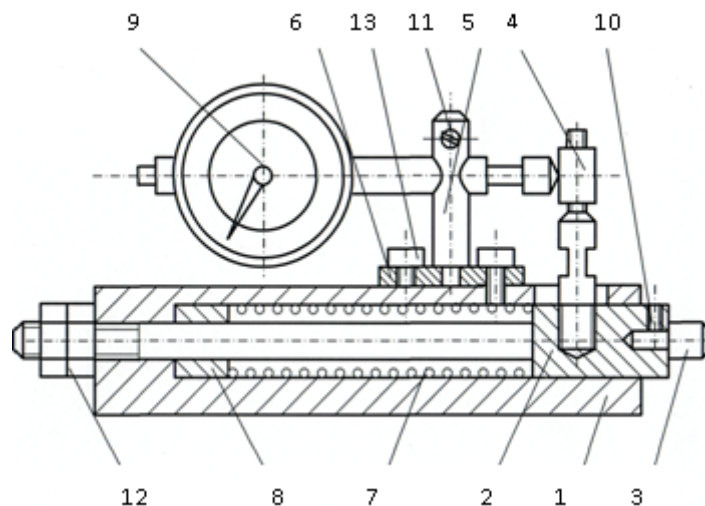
Схема алмазного выглаживателя: 1 – корпус; 2 – держатель выглаживателя; 3 – алмазный выглаживатель; 4 – стойка; 5 – стойка индикатора; 6 – основание; 7 – пружина; 8 – сменная проставка; 9 – индикатор; 10 – винт стопорный; 11 – винт стяжной; 12 – гайка регулировочная; 13 – винт
